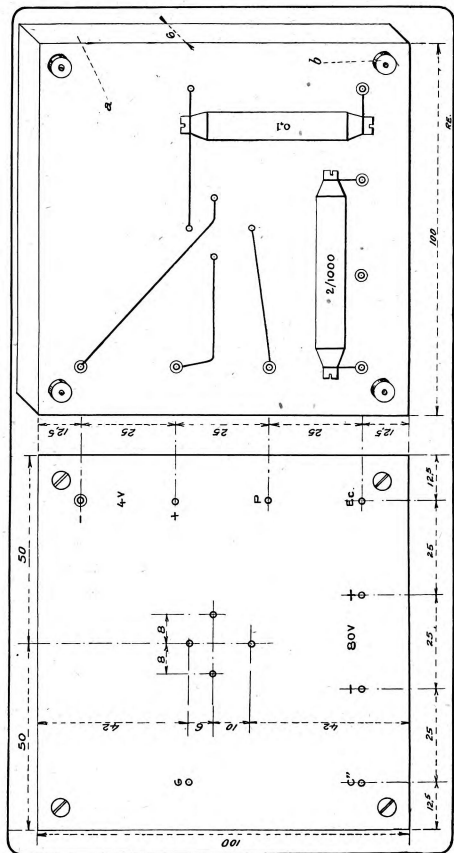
SUPPORT DE LAMPE DÉTECTRICE. — 1, vue de dessus; 2, vue de dessous. — a , éclouette ou bakélite; b , cules; d , épaisseur, bouchons de caoutchouc.
